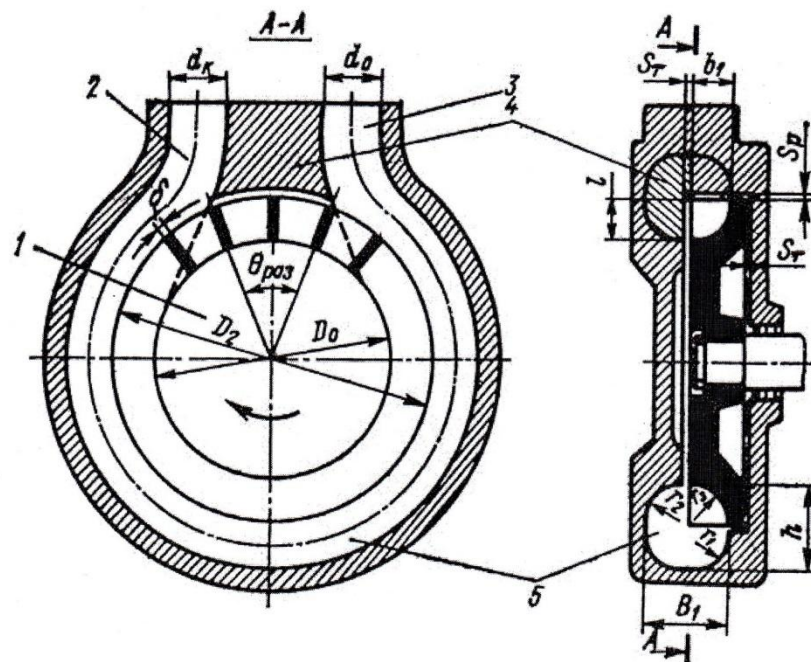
Конструктивна схема ступеня вихрового компресора
